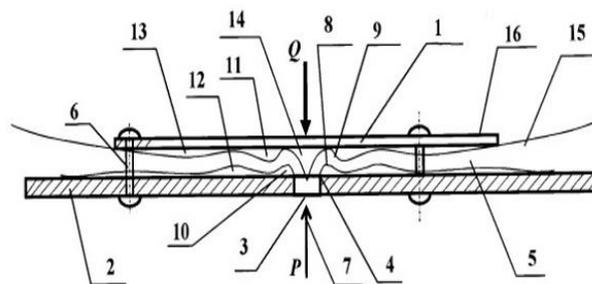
Закрепленный жесткий, упругий или эластичный клапан
